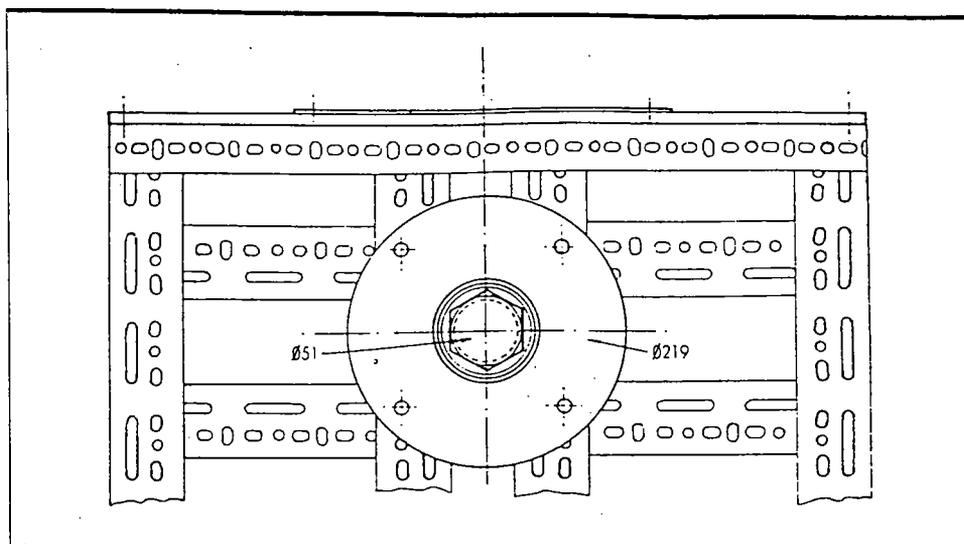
Detalle del dispositivo de fijación de la rueda de ensayo.
